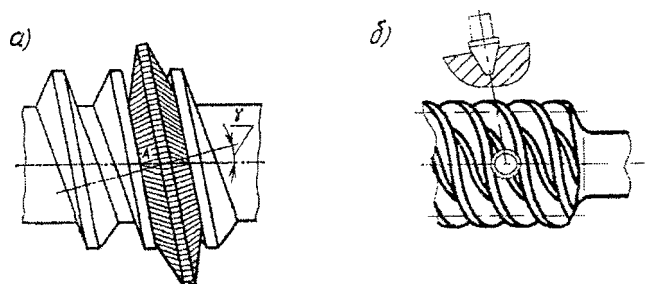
Схема установки дисковой фрезы с прямолинейным профилем при нарезании червяка ZK1 (а) и пальцевой фрезы при нарезании червяка ZK2 (б)
